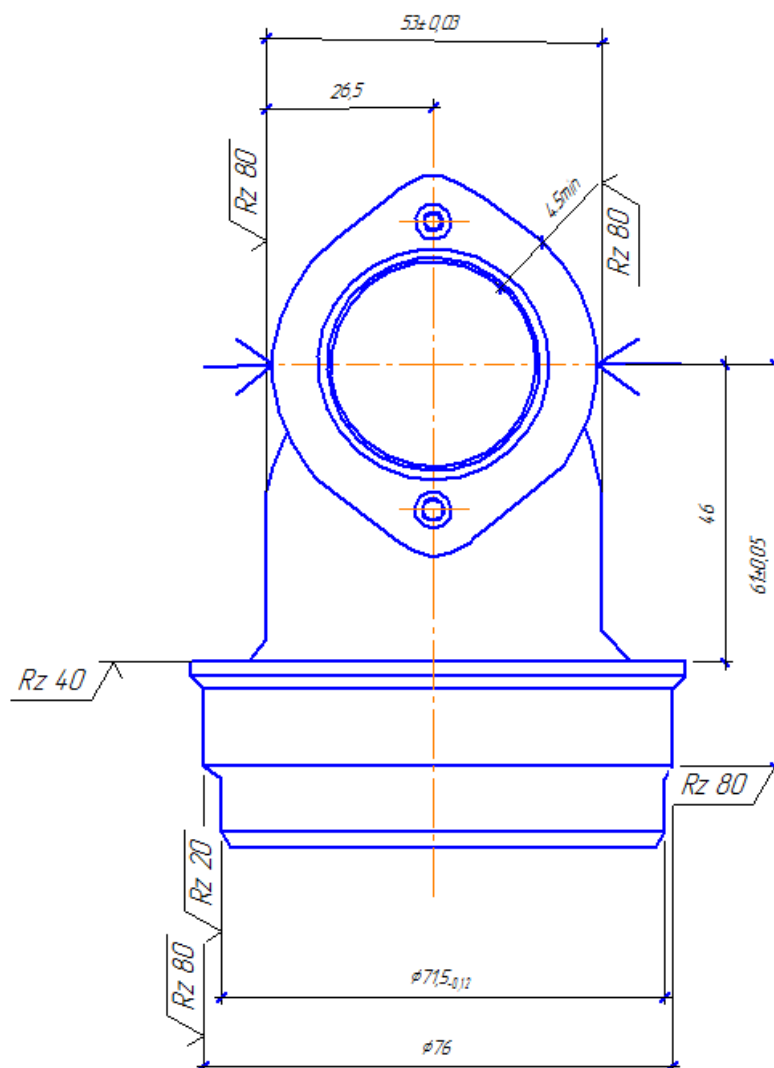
Схема установки заготовки при обработке отверстия $\text{Ø}35$ мм
